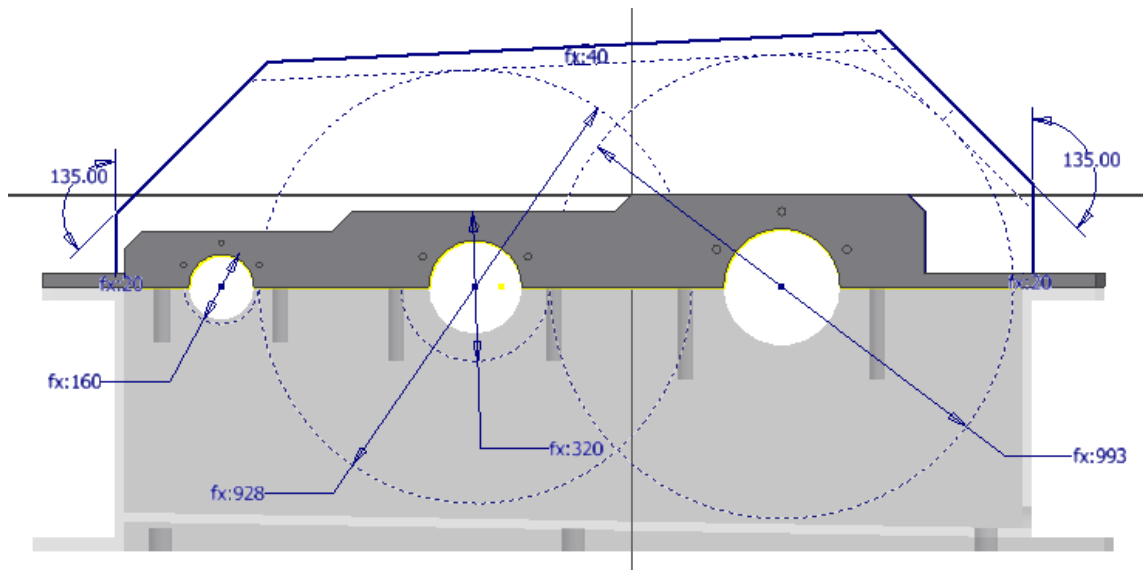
Croquis de la plancha soldada de la tapa de la carcasa.
